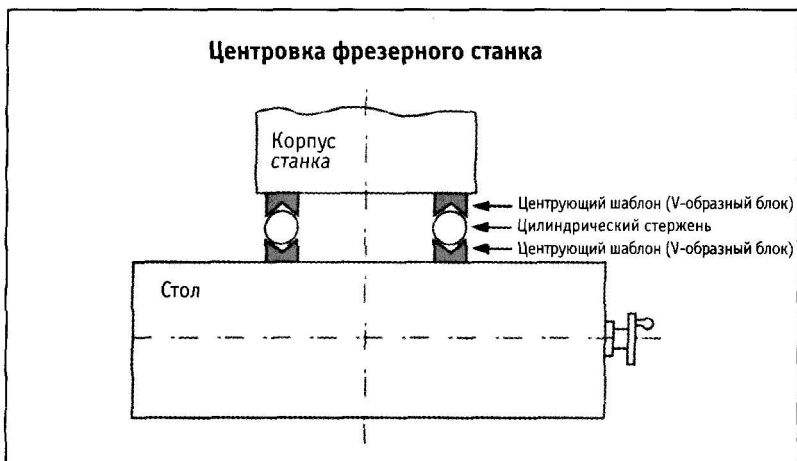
Использование центрующих шаблонов (V-образных блоков) для центровки стола и резца фрезерного станка
